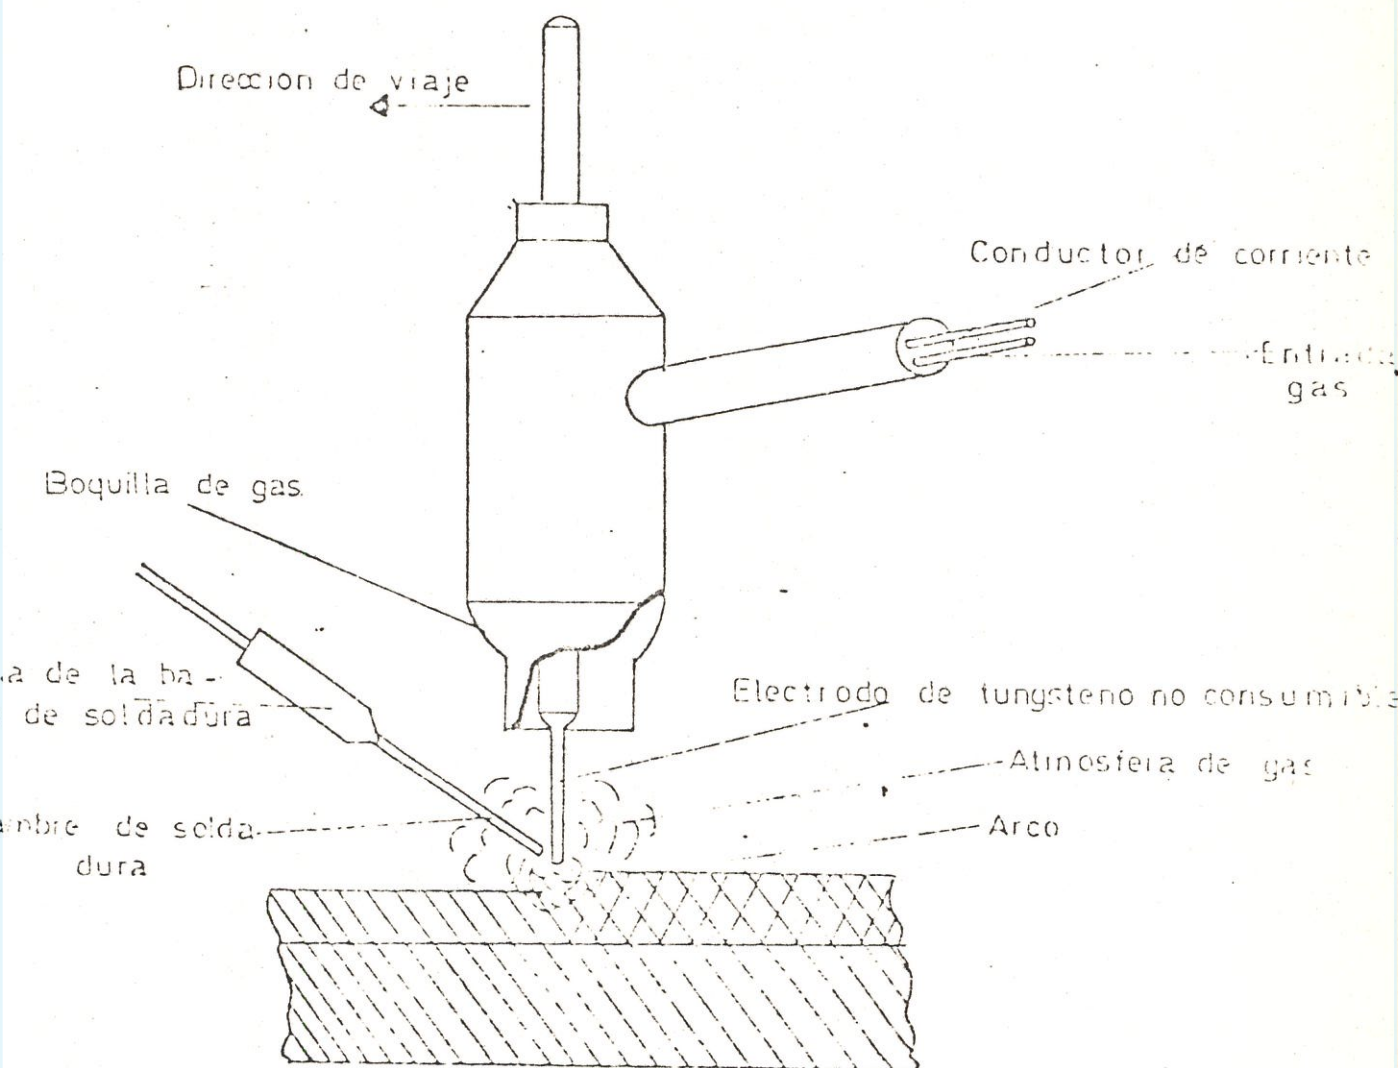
SOLDADURA AL ARCO CON GAS PROTECTOR (14)
